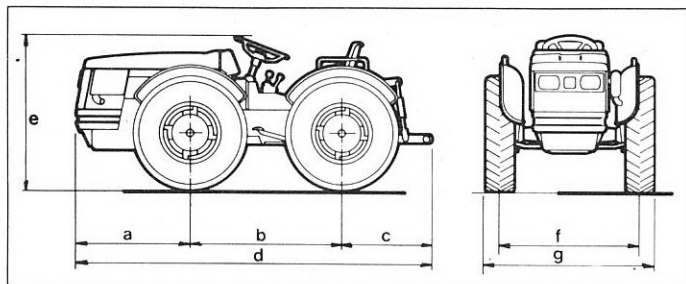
Dimensions hors tout du Tigre - Tigrone P.C.
